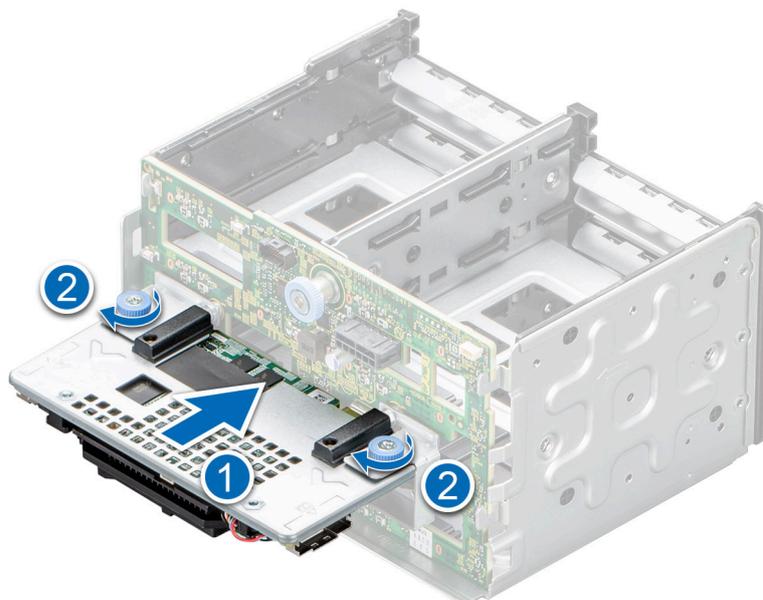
Installieren des PERC-Frontmoduls für die 2,5-Zoll-Laufwerkrückwandplatine.
